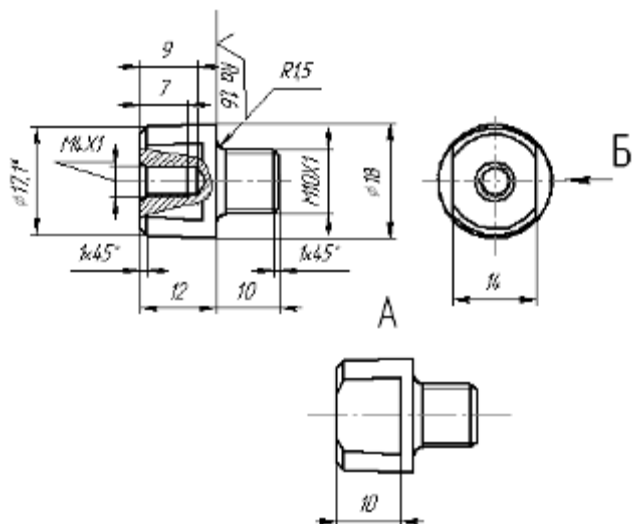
Конструкция державки для крепления унифицированного инструмента
